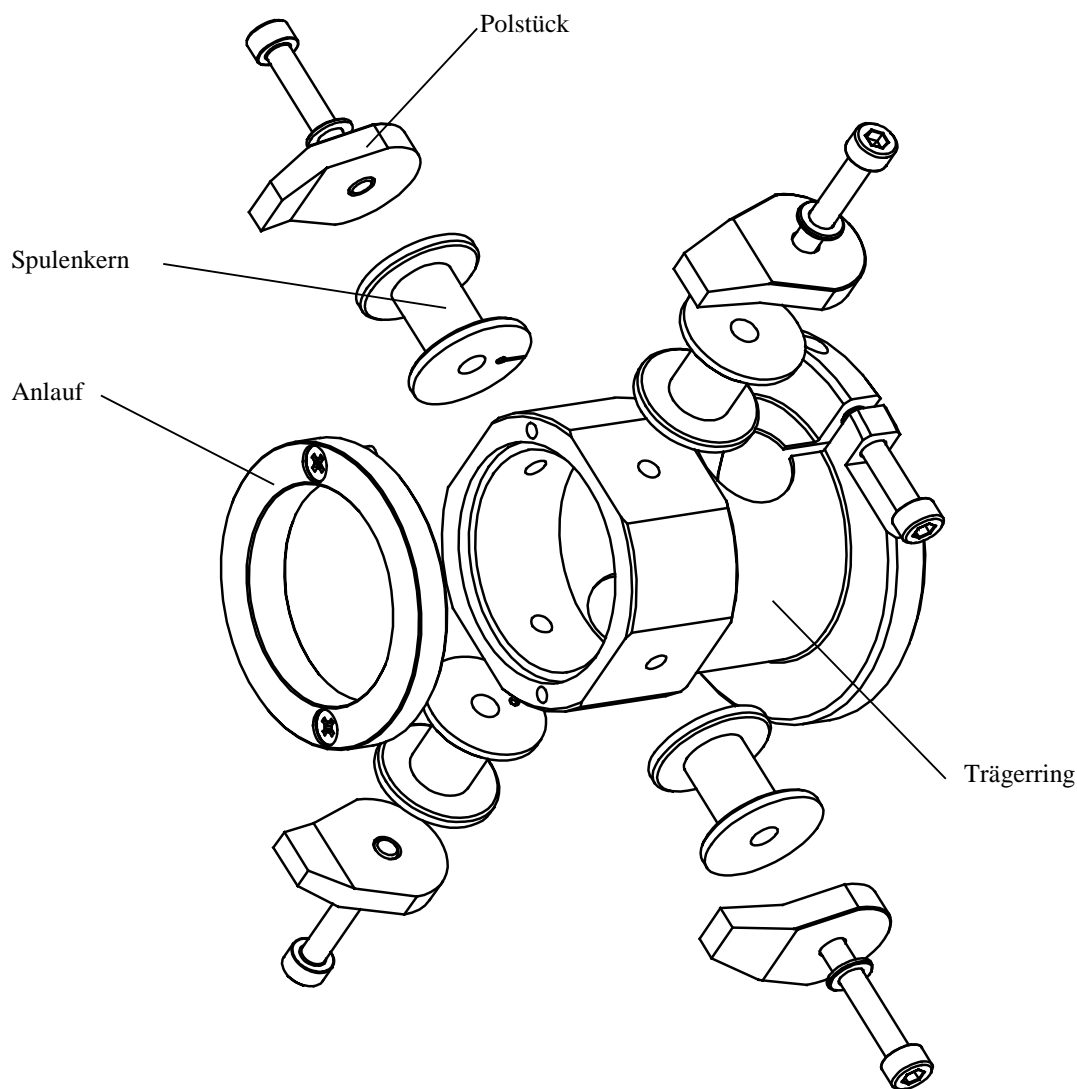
Explosionszeichnung der Wirbelstrombremse zur Vermeidung von Klapper- und Rasselgeräuschen an einer Zahnradstufe
